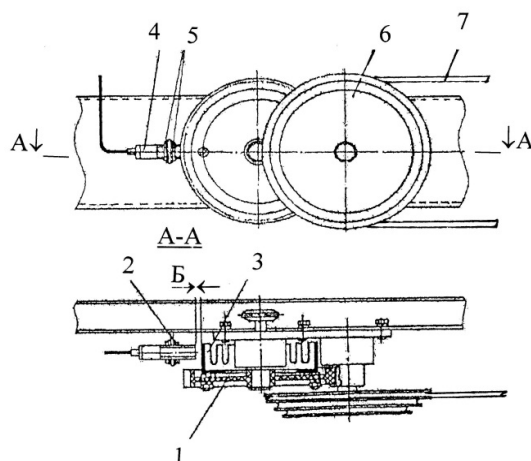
Установка и регулировка датчика импульсов обматывающего аппарата:
